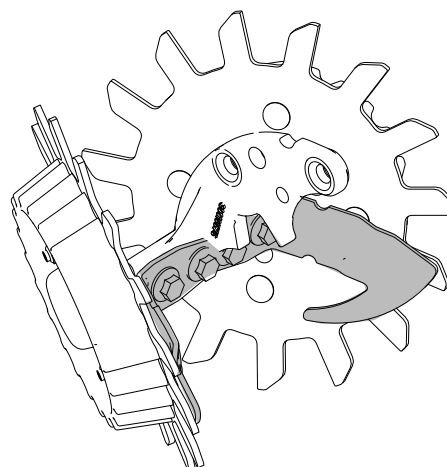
Rameno zapravovacího kola, pevné krátké nebo nastavitelné dlouhé.
